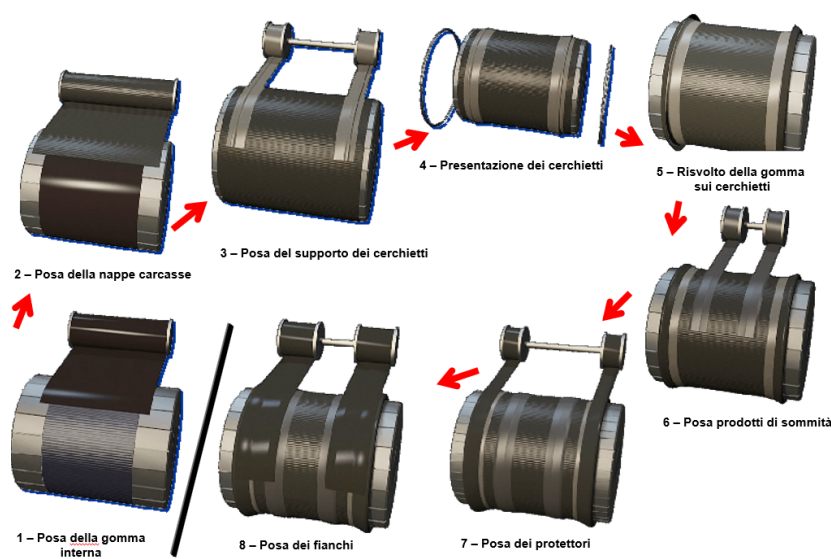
Prima fase di assemblaggio di uno pneumatico
